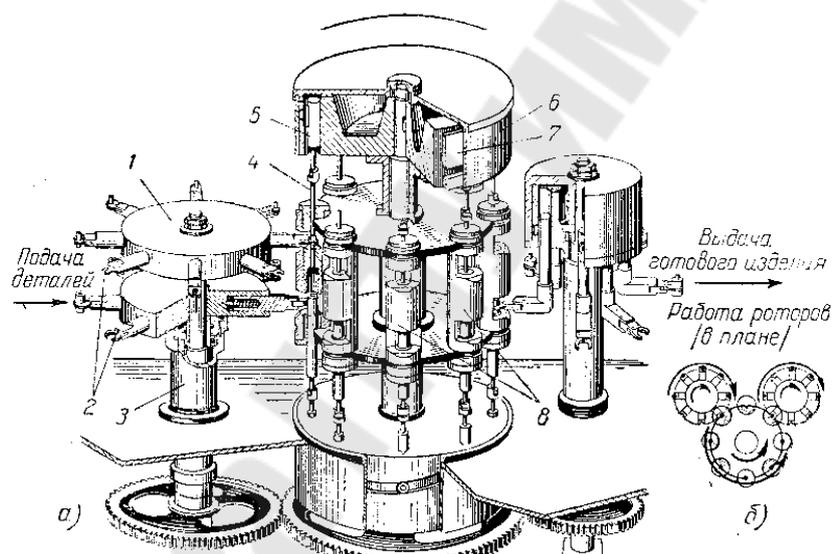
Типовой ротор для сборки двух элементов и обслуживающие его транспортные роторы: а – конструкция ротора; б – схема работы роторов в плане: 1 – диски; 2 – клещевые несущие органы; 3 – стакан; 4 – рабочий инструмент-пуансон; 5 – ползун; 6 – барабан; 7 – неподвижный пазовый копир; 8 – блоки рабочего инструмента
